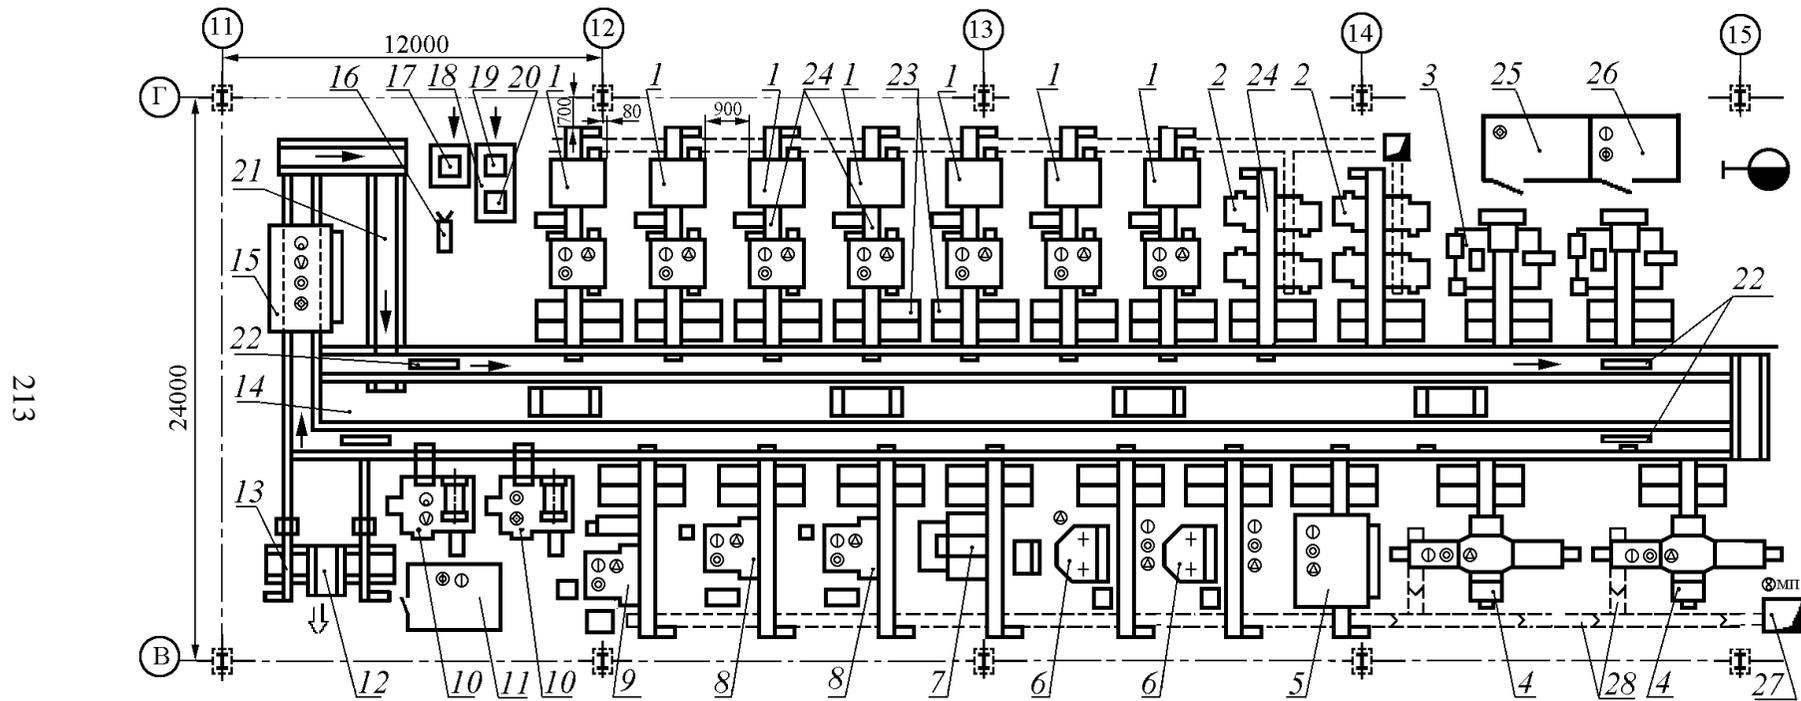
П14. ГПУ для обработки корпусных деталей цилиндрической формы:
